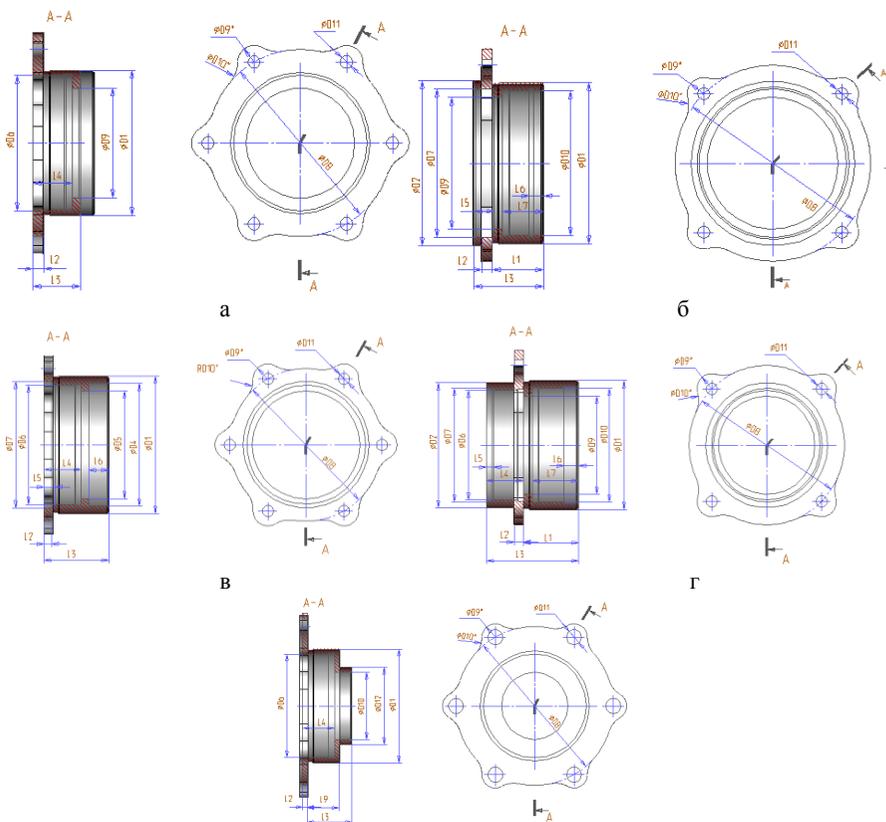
Варианты 3D моделей и чертежей стаканов подшипника
